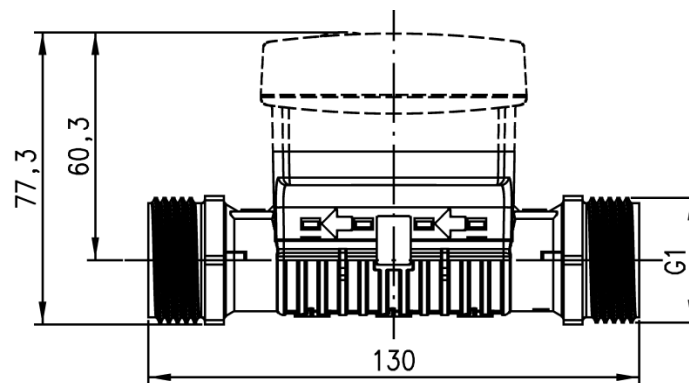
Übersicht Maße Baulänge 130 mm (Gewinde)
